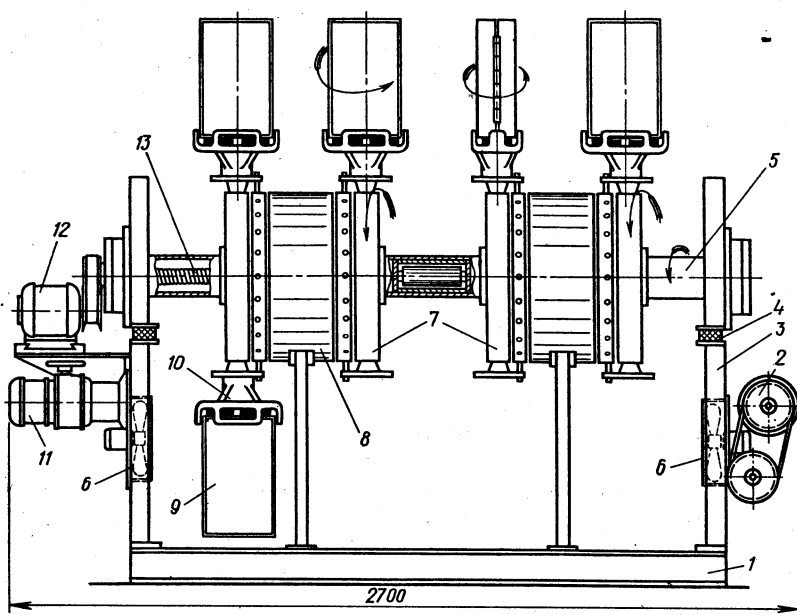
Ротационный агрегат модели HS-III с планетарным движением формодержателей для изготовления пустотелых шоколадных фигур центробежным способом:
